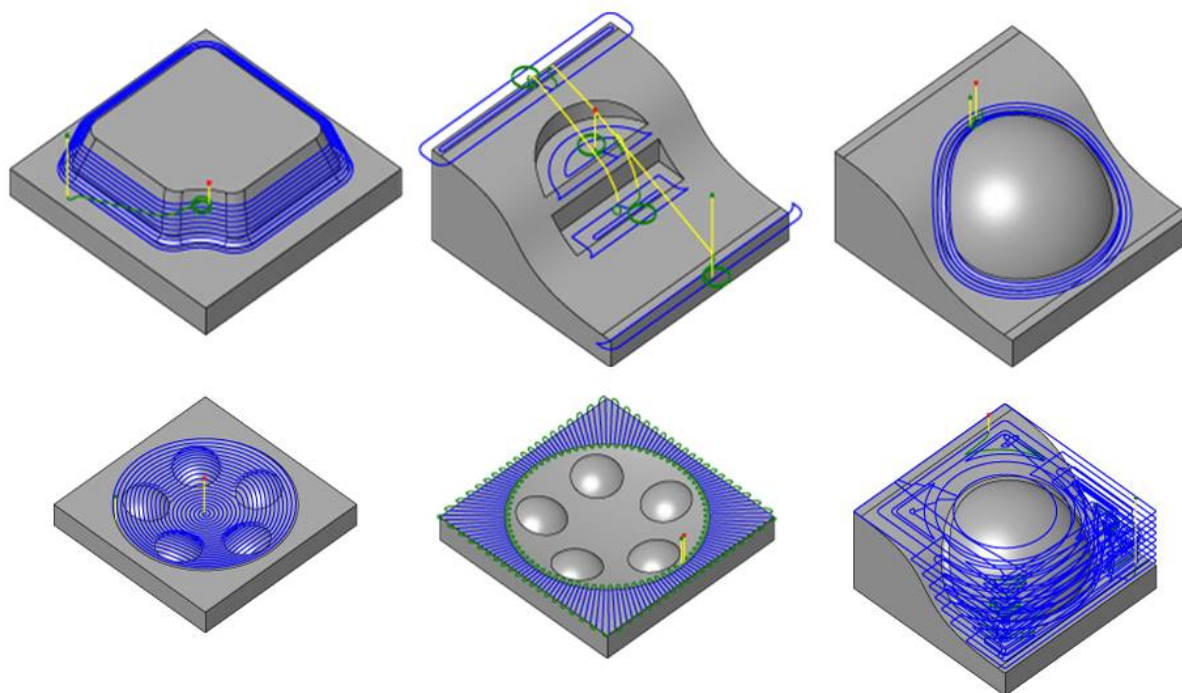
Различные виды стратегий 3-х координатной чистовой фрезерной обработки
